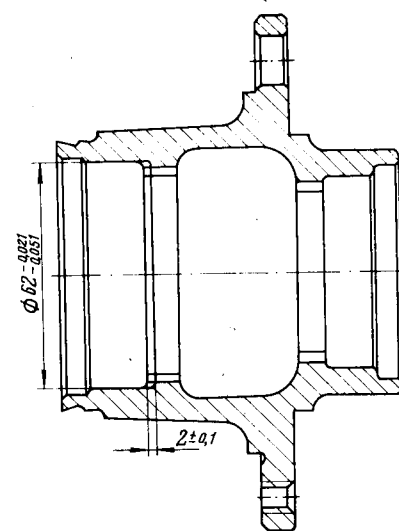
Дополнительная обработка ступицы для замены шариковых подшипников на роликовые
